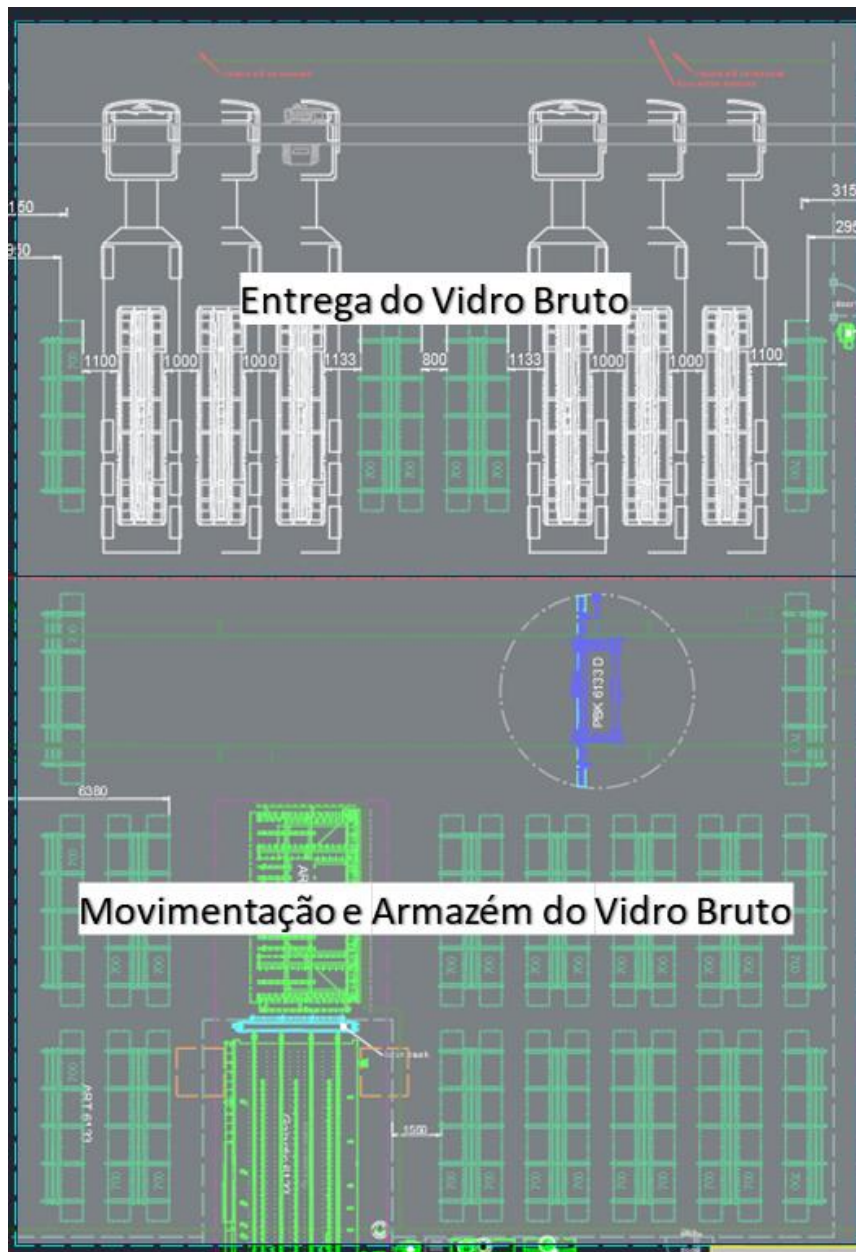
Zona de entrega e armazenamento de vidro bruto.
